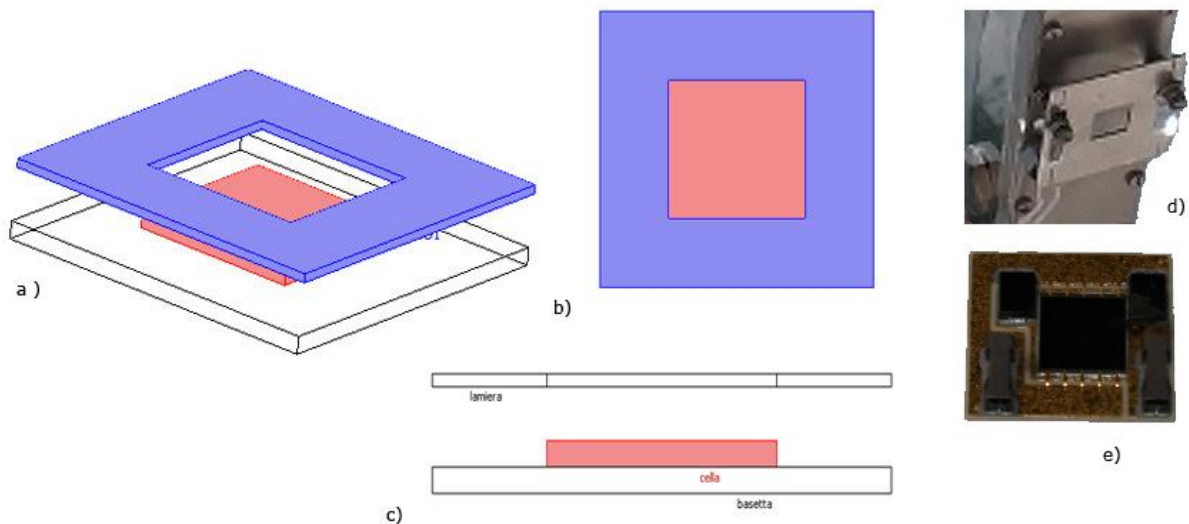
cella con protezione in lamiera a) prospettiva b) vista dall'alto c) vista laterale d) protezione in lamiera con dissipatore e) cella utilizzata
